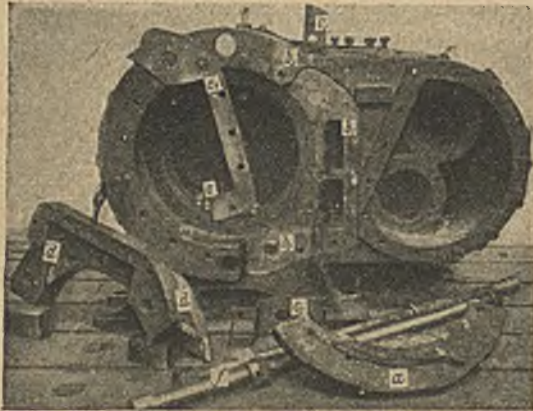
Schweißung einer Kesselpumpe.
